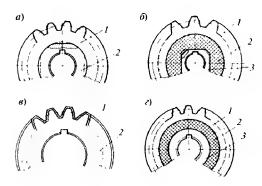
Шлифовальный шевер с наружным расположением зубьев:
